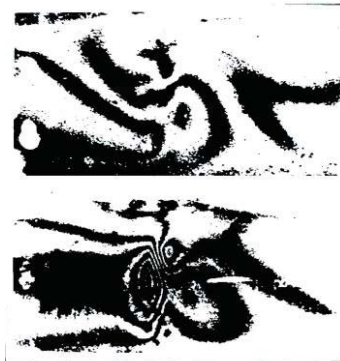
Evaluación de la integridad de tubos de acero soldados. Imagen superior una soldadura correcta. En la imagen inferior una mala soldadura. La soldadura defectuosa se caracteriza por una deformación excesiva que se visualiza por una imagen con trazas muy densas [Hung 2004].
